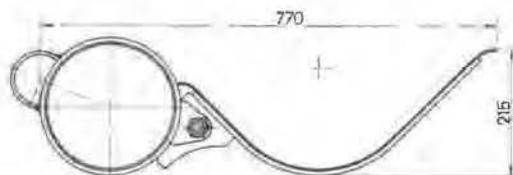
Assemblage du tube au couloir en « demi-lune ».
